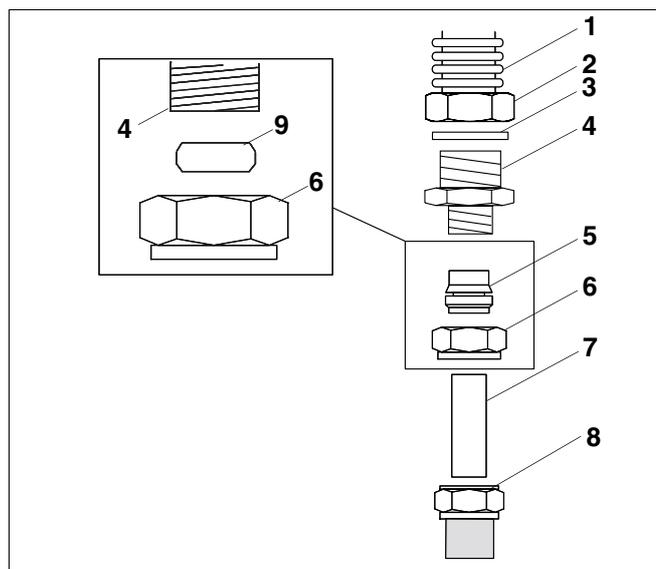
Raccord Twin Tube DN 20 sur écrou-raccord avec bague de serrage 18 mm
